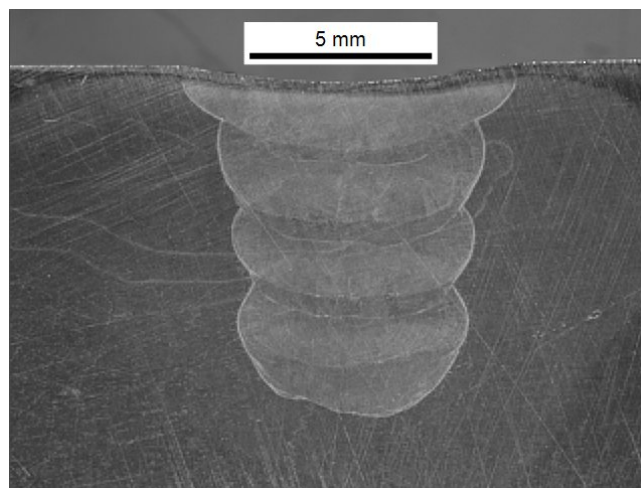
Macrographie d'une opération de soudage pour le remplissage du chanfrein étroit.
